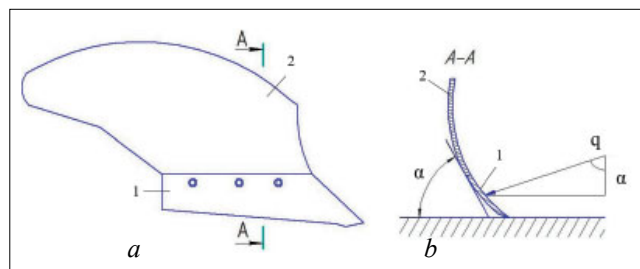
Лемешно-отвальная поверхность: а – вид спереди; б – вид с торца; 1 – лемех; 2 – отвал;  $\alpha$  – угол наклона плужного корпуса к дну борозды;  $q$  – нормаль к усредненной поверхности корпуса плуга
